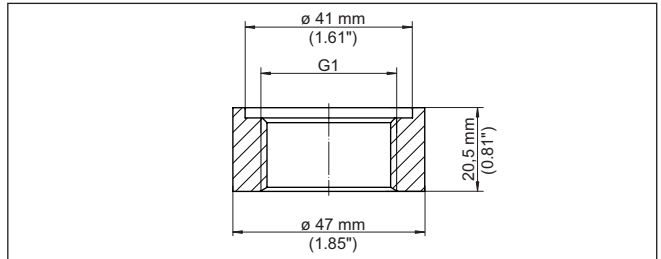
Maße Einschweißstutzen G1 (ISO 228)
